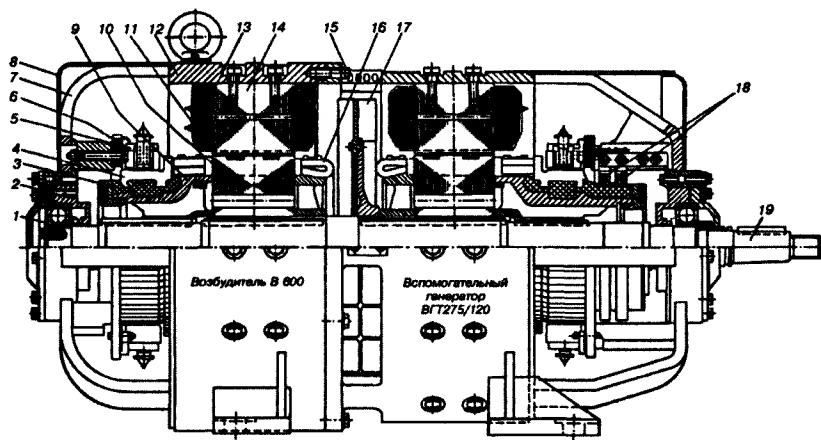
Двухмашинный агрегат типа А706Б:
